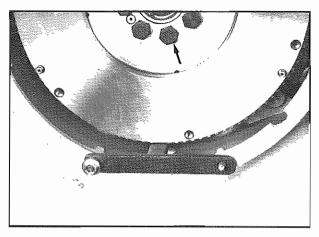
Viti di bloccaggio volano Flywheel locking screws
